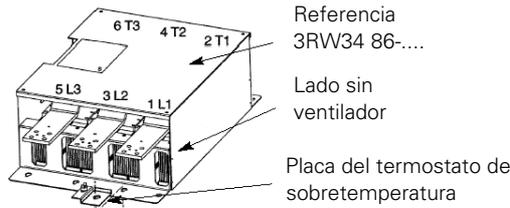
Montaje del termostato de sobretemperatura para 3RW34 86
